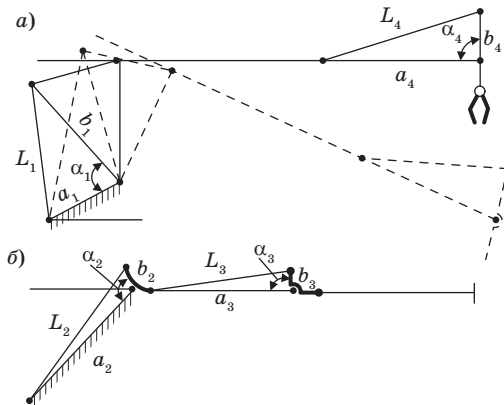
Конструктивная схема манипулятора: а – вид сбоку; б – вид сверху
